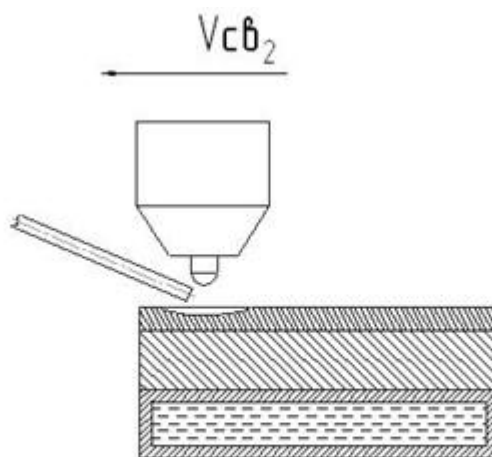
Схема сварки на охлаждаемой подкладке
